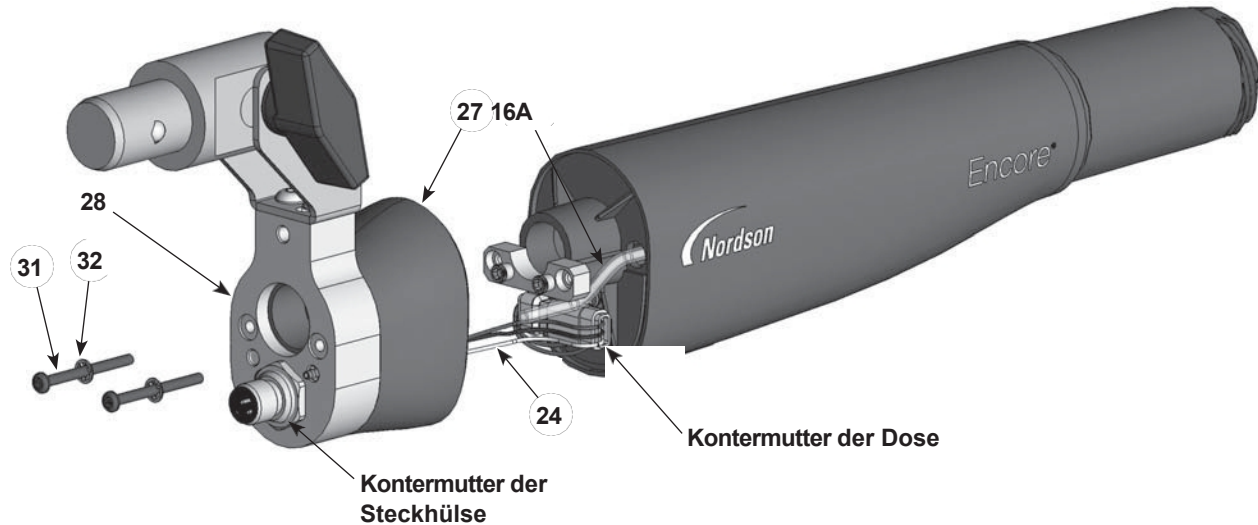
Demontage der Pistole - Austausch des Pulverrohrs
